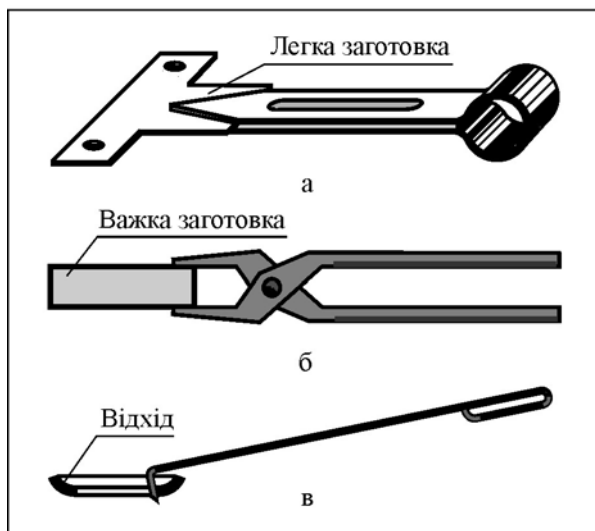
Ручний інструмент, що захоплює: а – пінцет; б – кліщі; в - гачок
